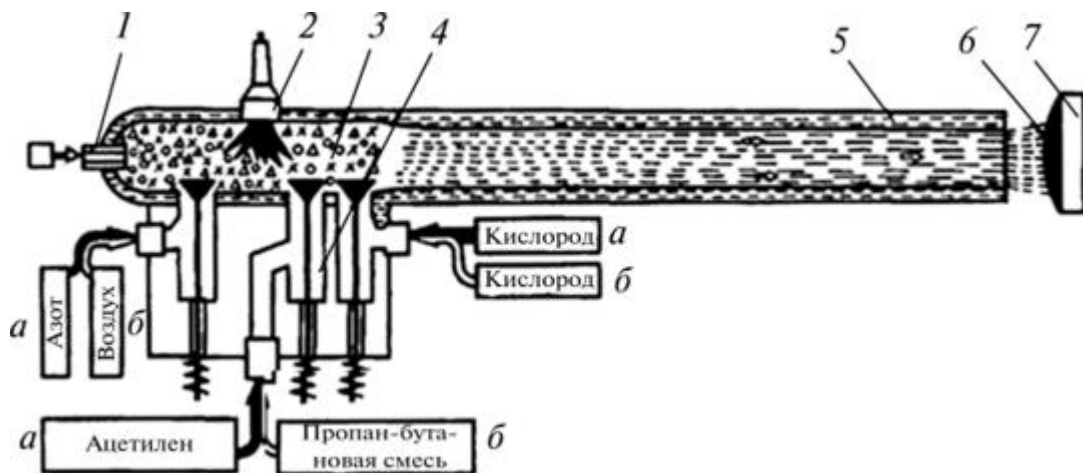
Схема плазово-детонаційної установки [23]: а – базова; б – оновлена; 7 – порошковий живильник; 2 – запальний пристрій; 3 і 4 – вибухова і змішувальна камери; 5 – водоохолоджуваний ствол; б – напілювані покриття; 7 – основа.
